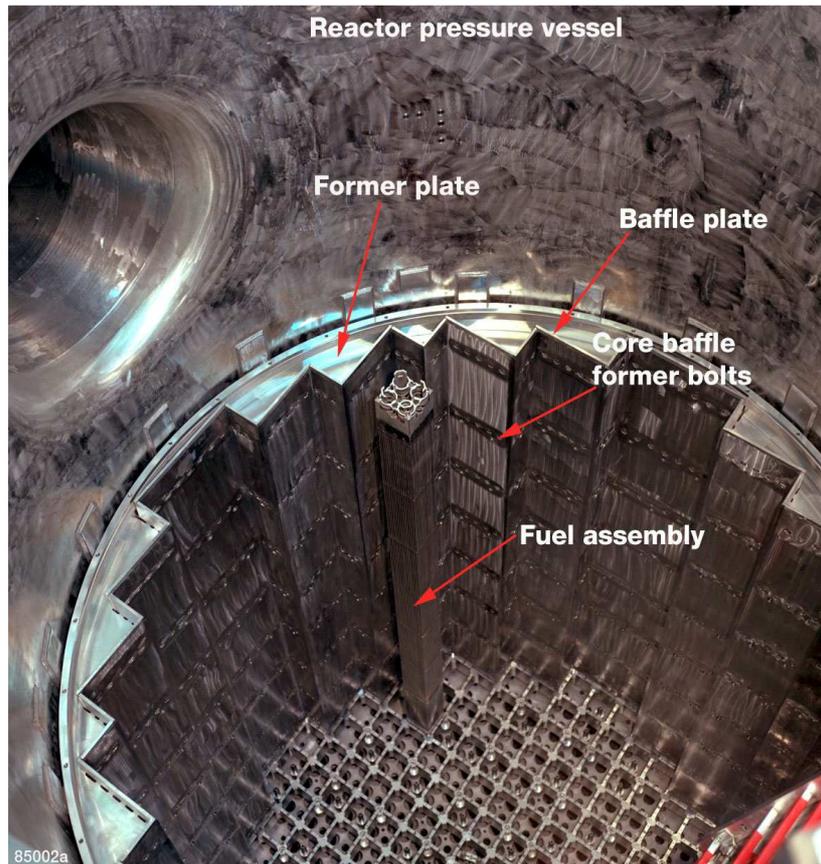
Kernbehälter, eingesetzt in Reaktordruckbehälter
